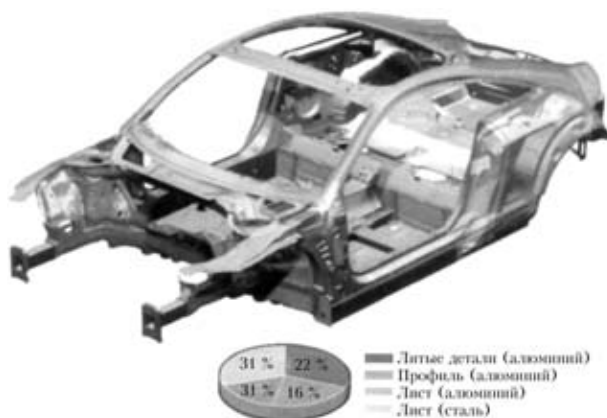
Конструкция корпуса Audi TT из разнородных металлов [4]
